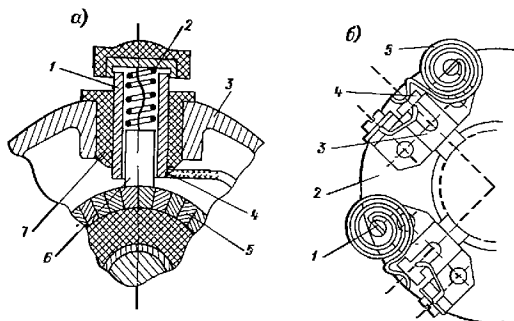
Щеткодержатели малых машин: а — трубчатый б — коробчатый
